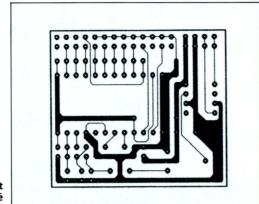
Circuit imprimé vu côté soudures.
